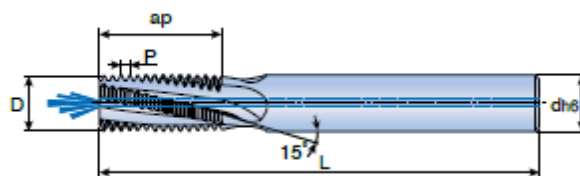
Резьбофреза МТЕСВ-ISO
